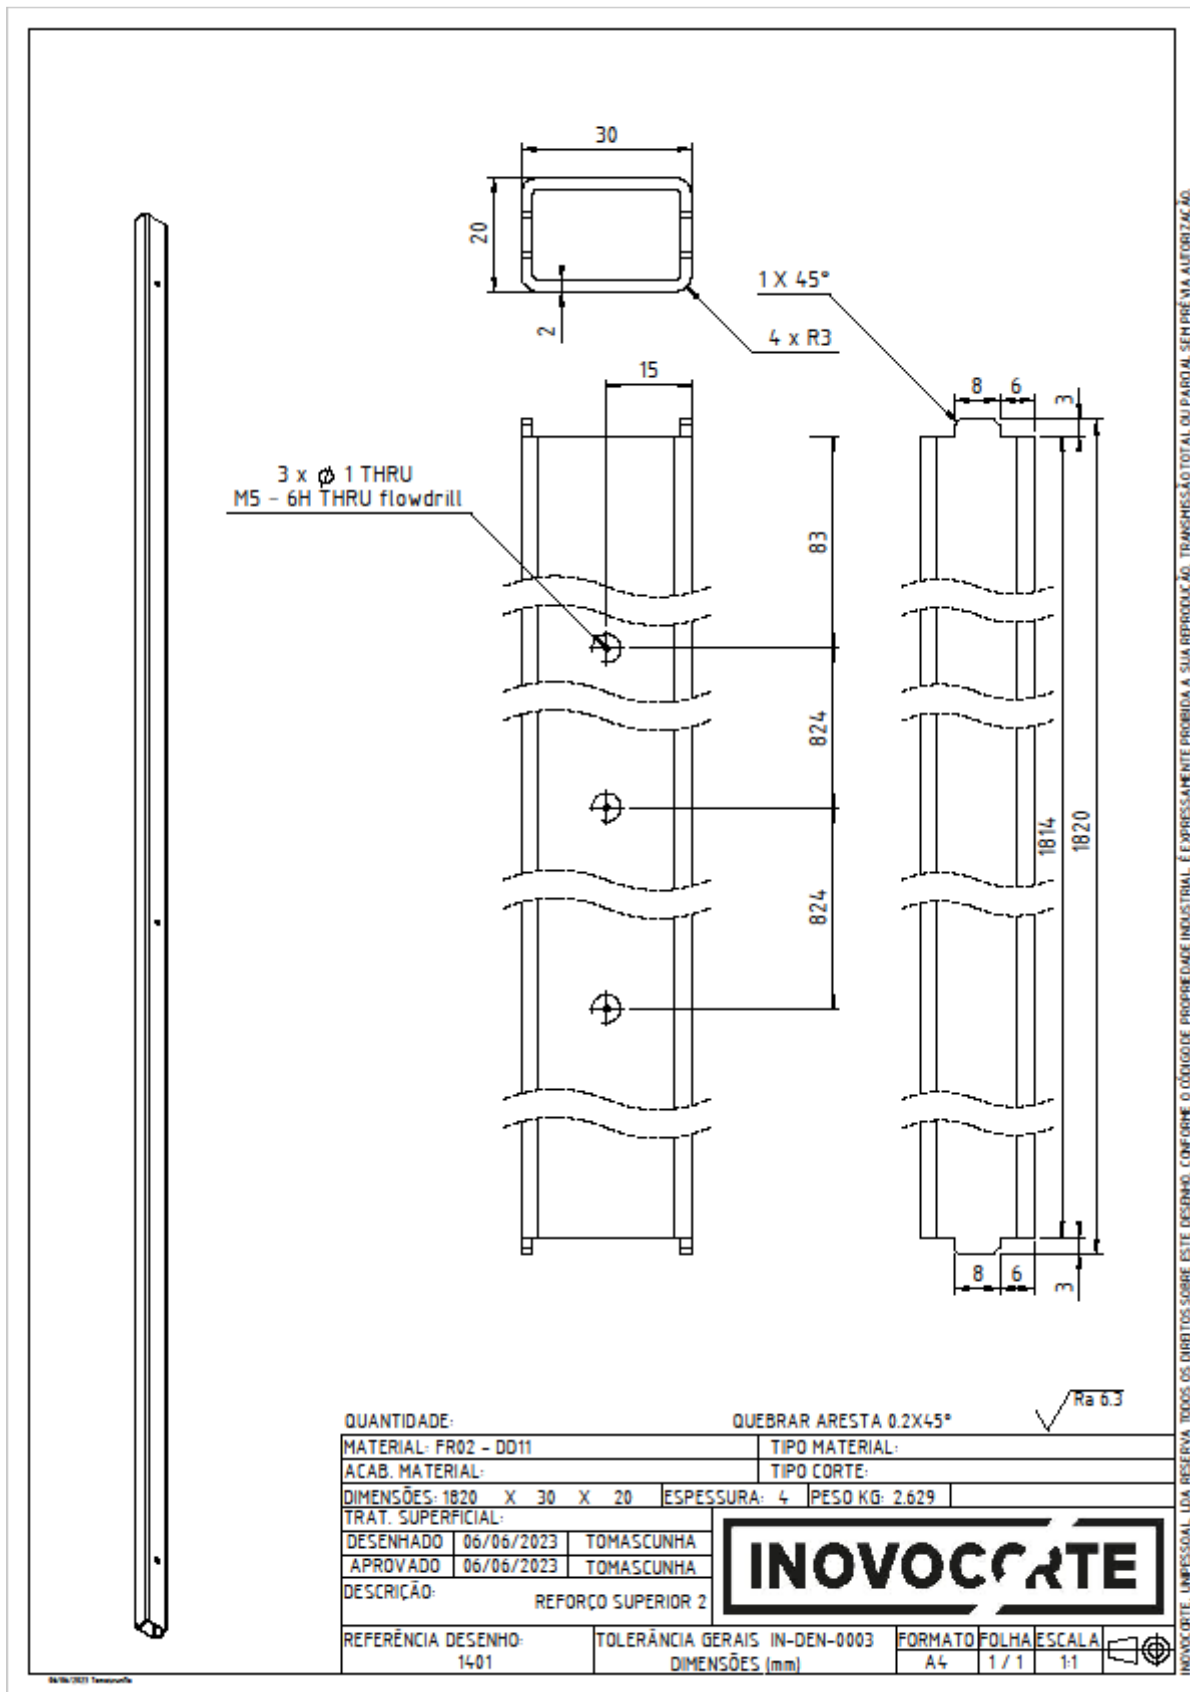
Desenho técnico do reforço superior 2 (1401).
